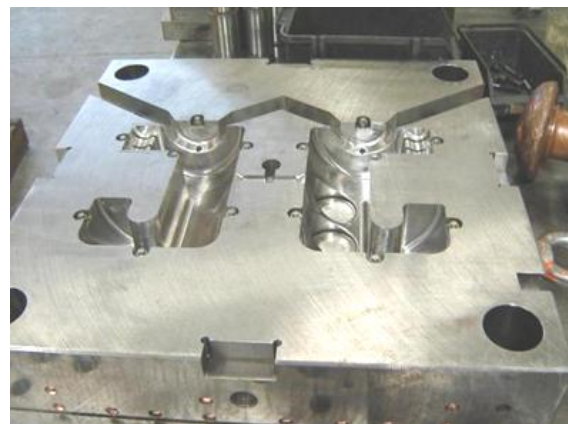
Metade fêmea do molde de injeção das metades principais do corpo do gabinete em processo de usinagem.
